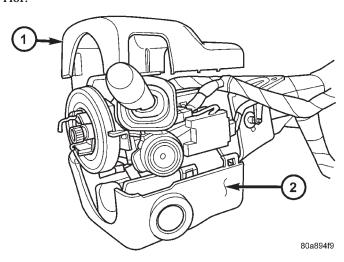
DESMONTAJE E INSTALACION DE CUBIERTA
